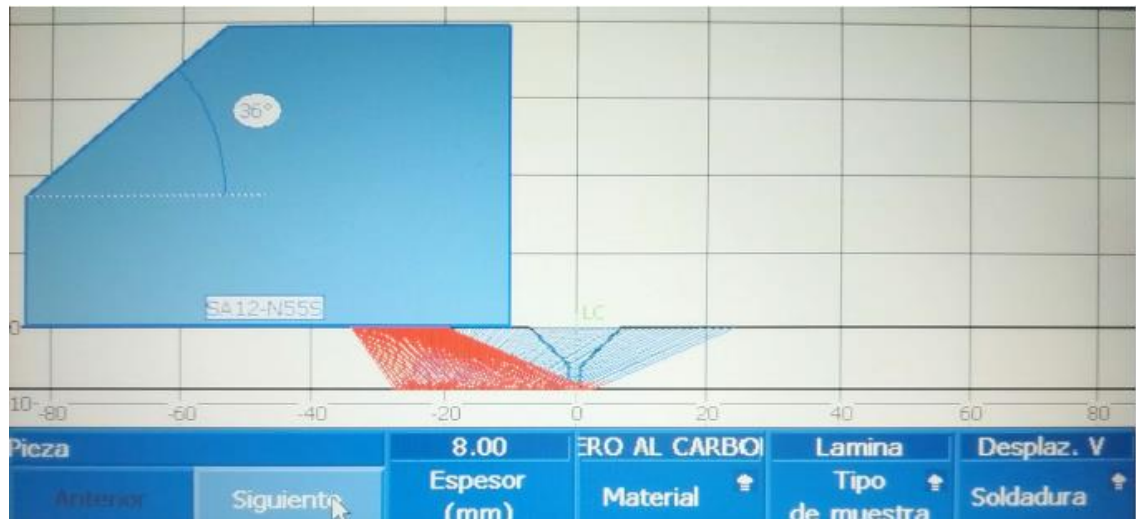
Configuración final para inspección de soldadura sobre placa de acero SAE 1020
